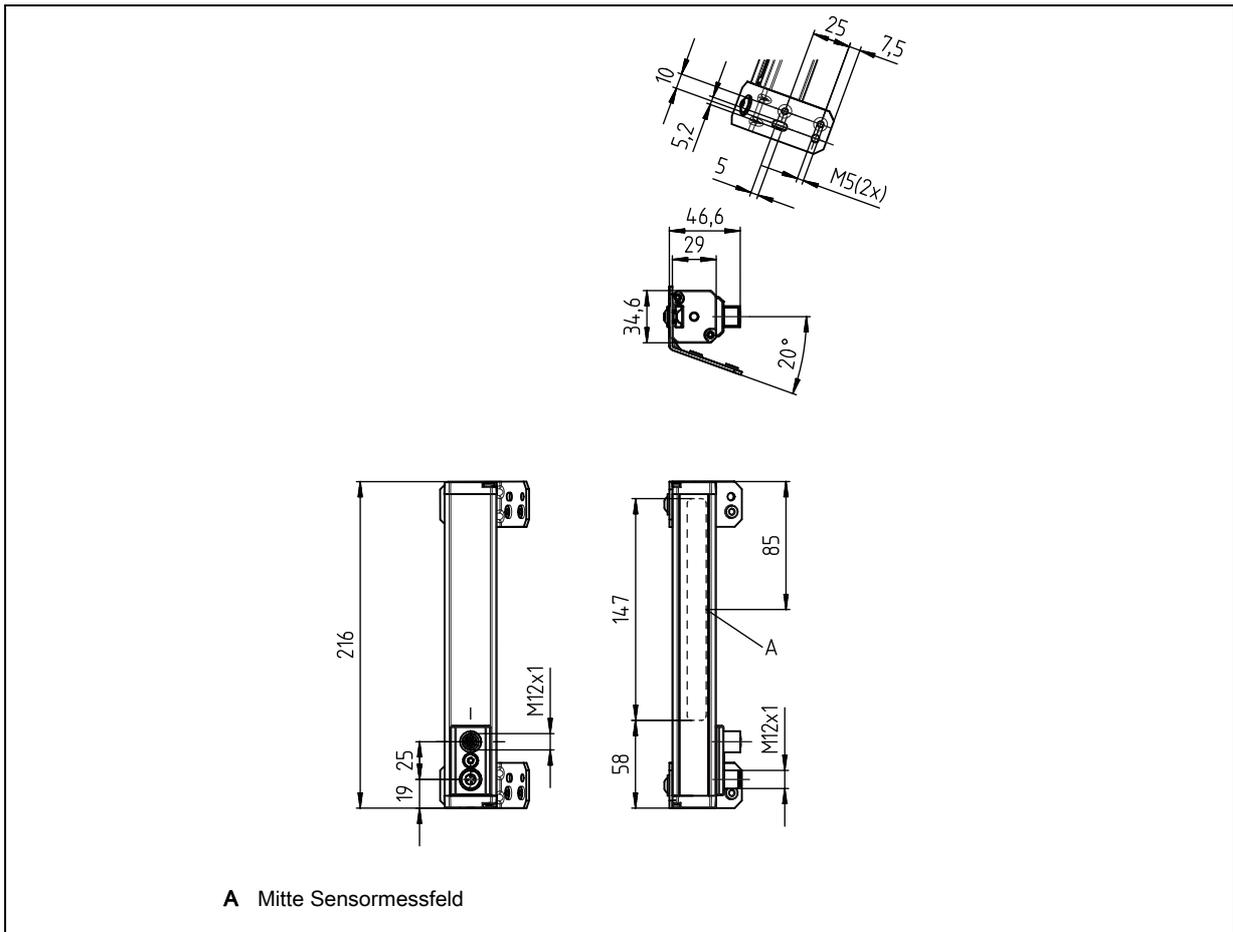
Maßzeichnung OGS 600-140/CN-M12 – kurze Ausführung
